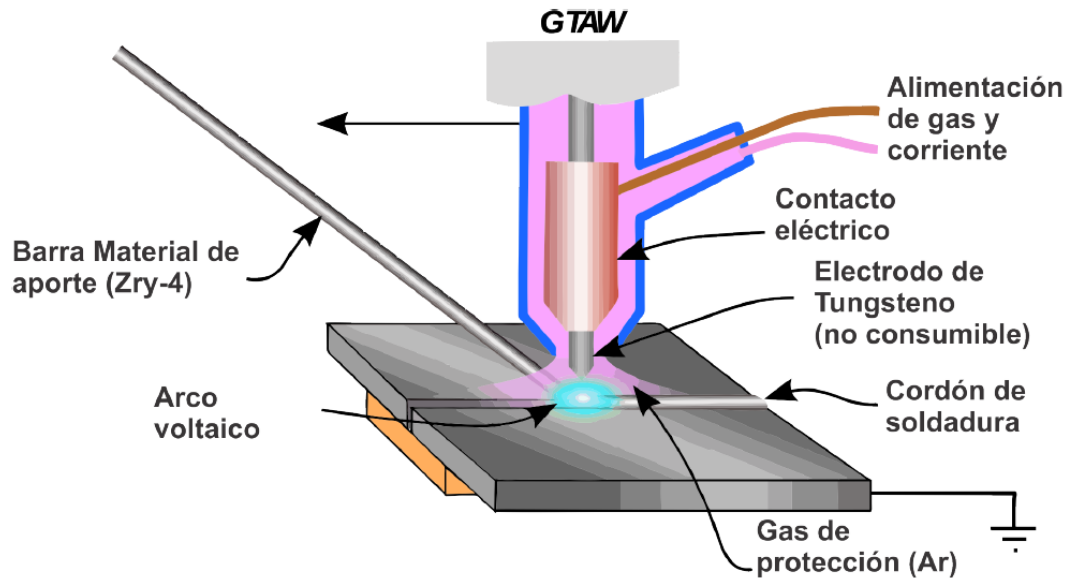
Esquema del proceso de soldadura tipo GTAW.
